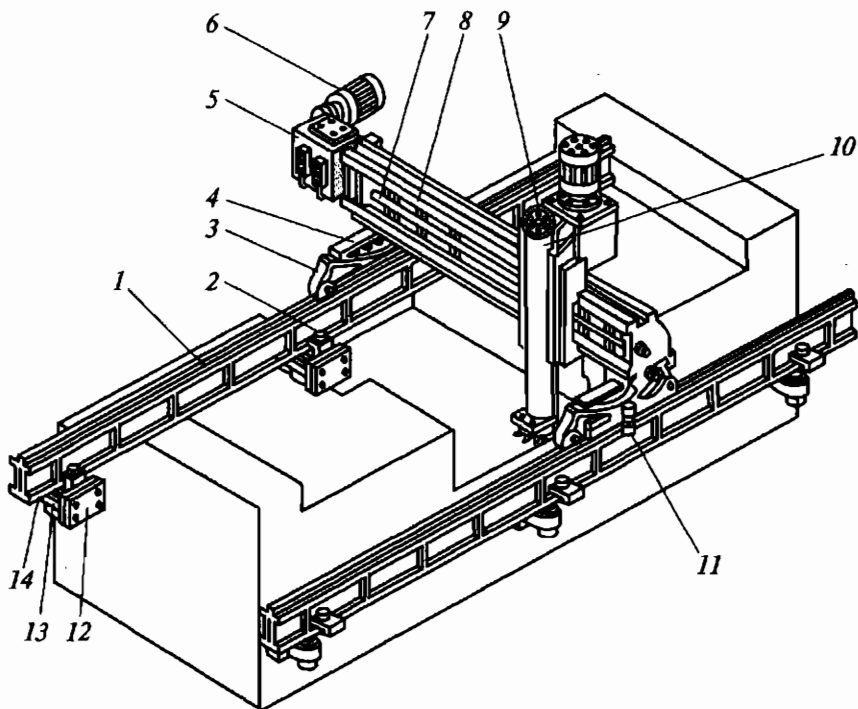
Приспособление для ремонта рабочих поверхностей шаботов молотов:
